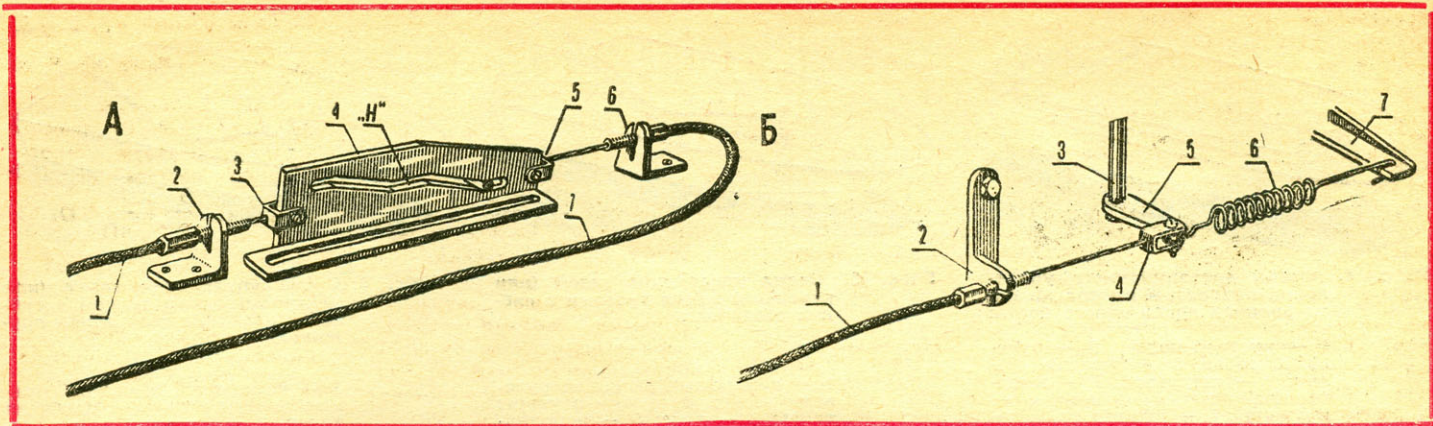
А. Общий вид механизма управления реверсом подвесного мотора «Вихрь» с помощью двух тросов в гибкой оболочке:
